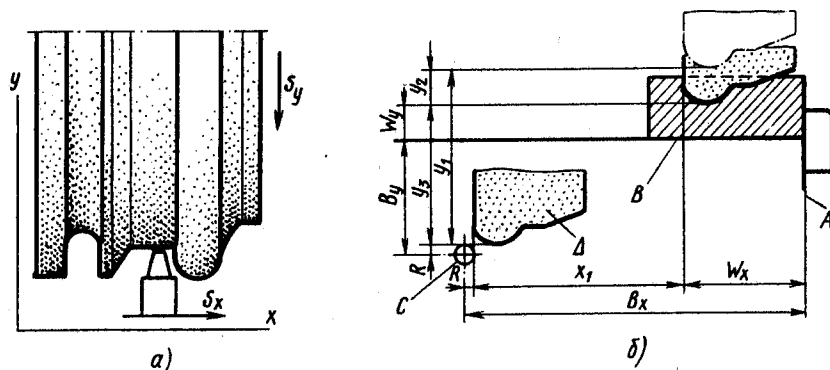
Правка рабочей поверхности круга (а) и наладка станка при профильном шлифовании на станке с ЧПУ (б)
